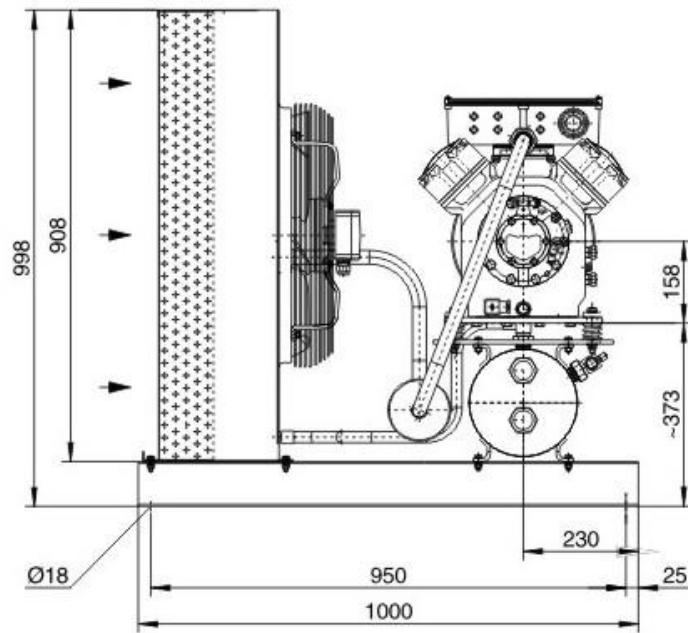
Компресорно-конденсаторний агрегат
